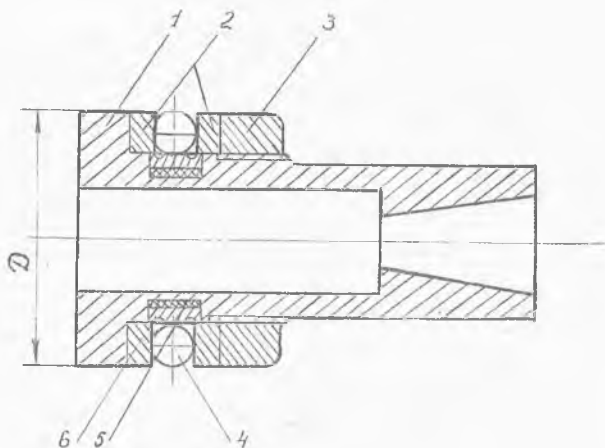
Конструкция ротационного упрочнителя: 1 — корпус упрочнителя; 2 — сепаратор; 3 — гайка; 4 — шарик; 5 — резиновая прокладка; 6 — отражатель
